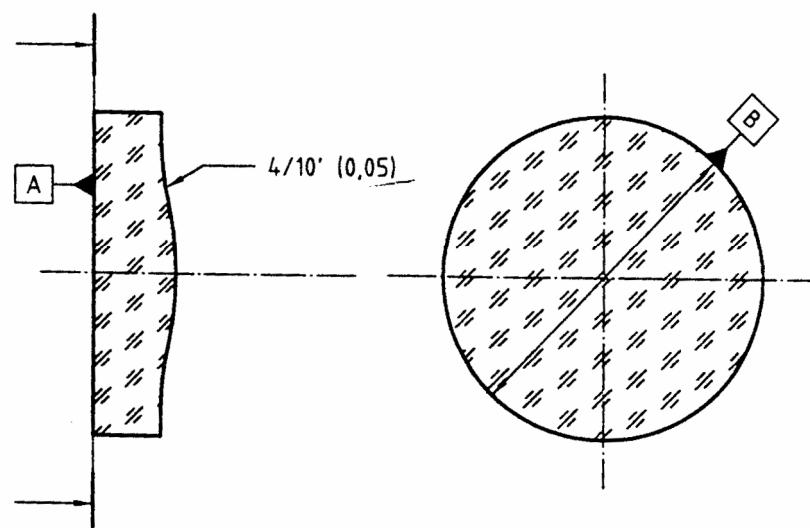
Допуск на центрировку асферической поверхности
